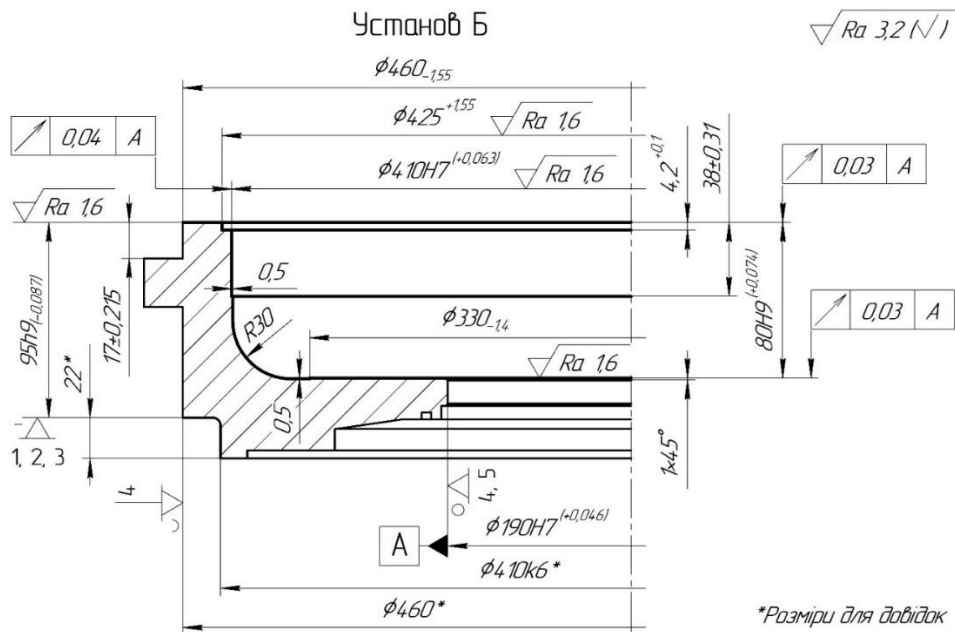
Ескіз заготовки на операції 025. Установ Б
